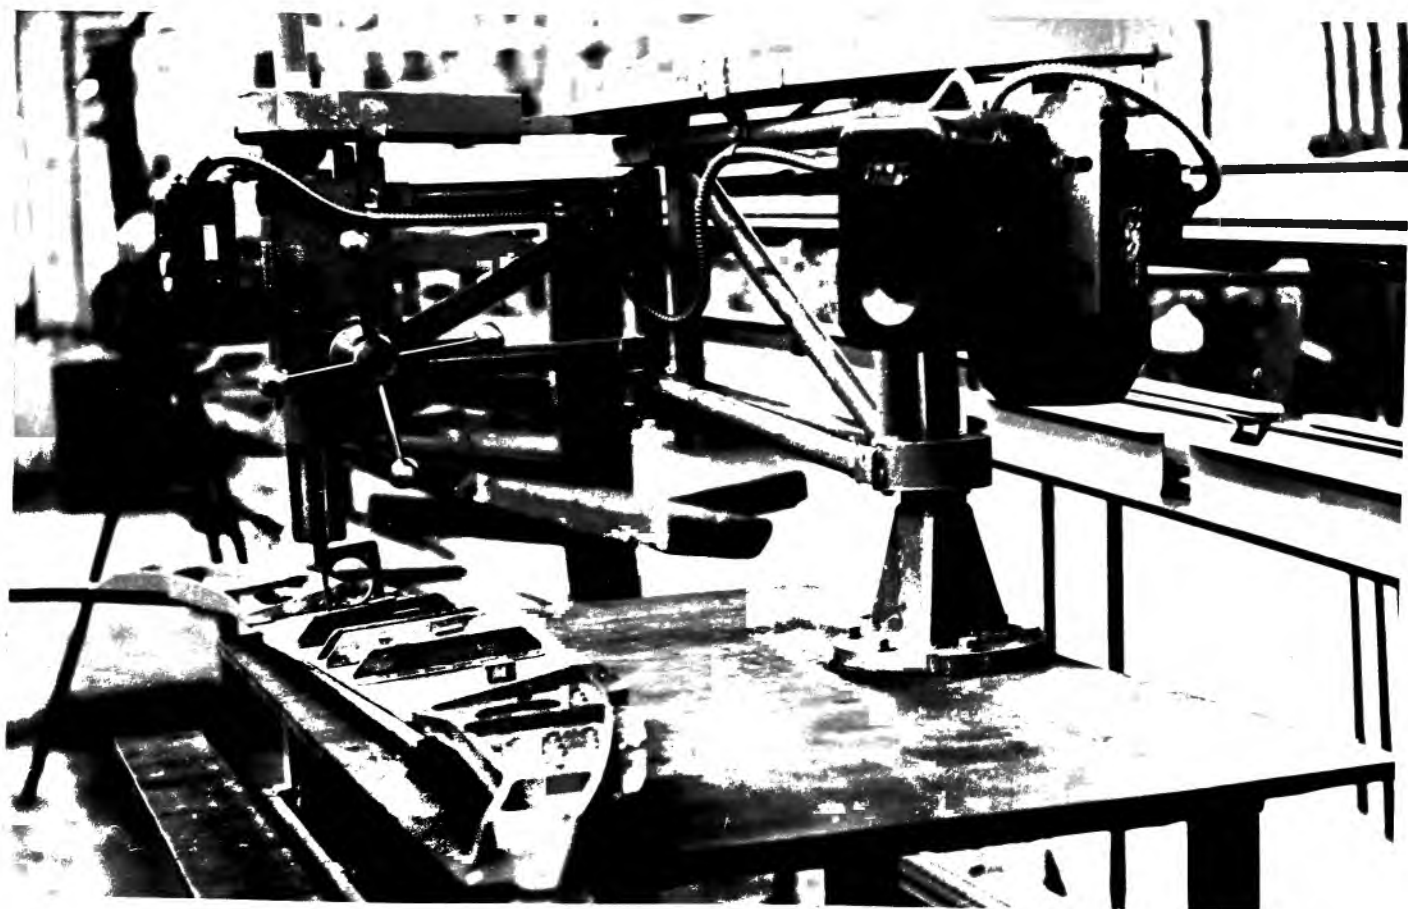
Хоботный малогабаритный станок для сверления подборок.
